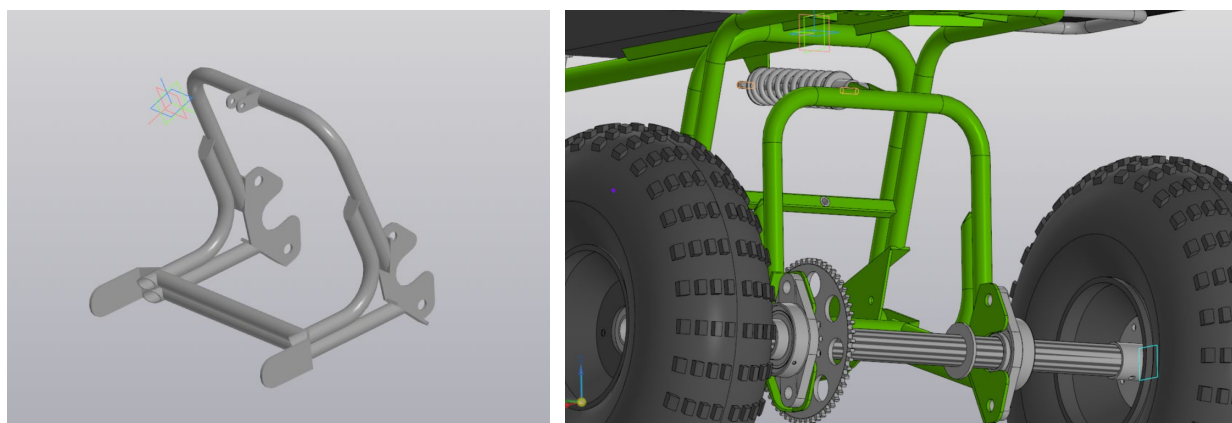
Кофр с опорой, крепящейся к несущей конструкции
